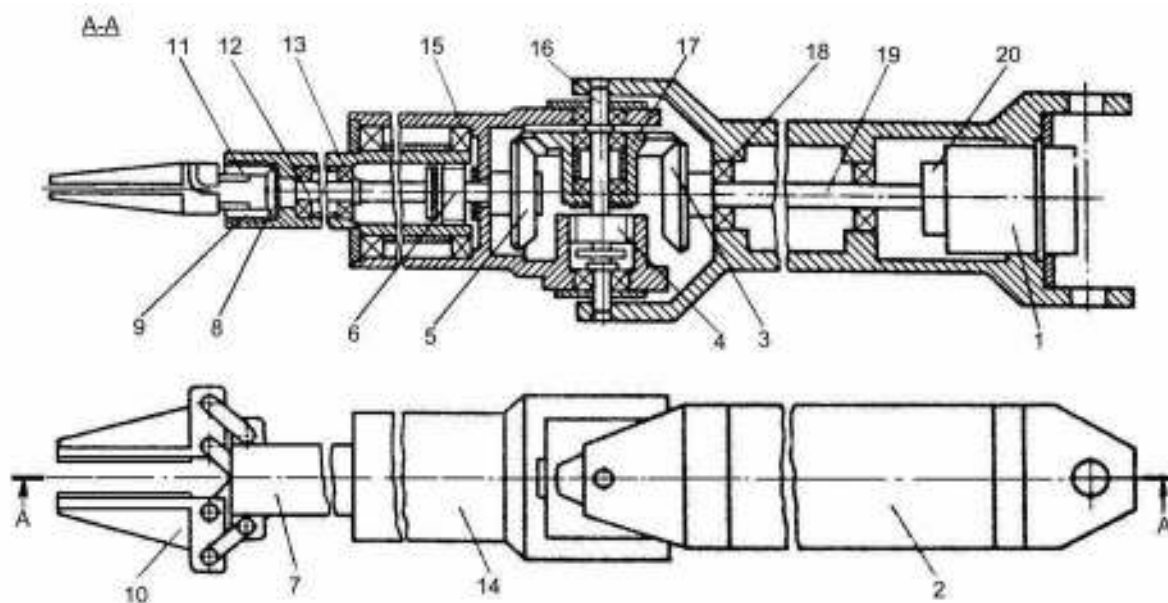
Сосредоточенный привод кисти манипулятора ПР
